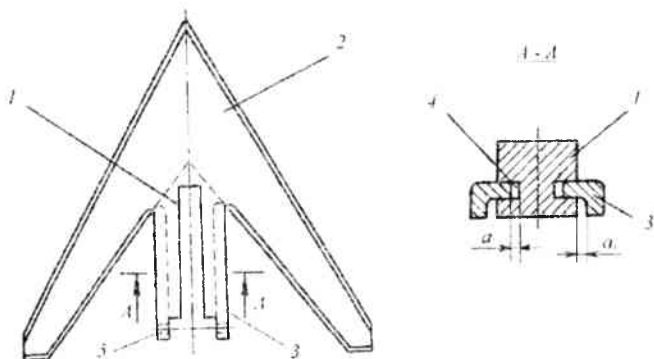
Быстросъемная лапа пассивного рабочего органа: 1 – стойка; 2 – лапа; 3 – хвостовик лапы; 4 – паза; 5 – отверстия для фиксатора
